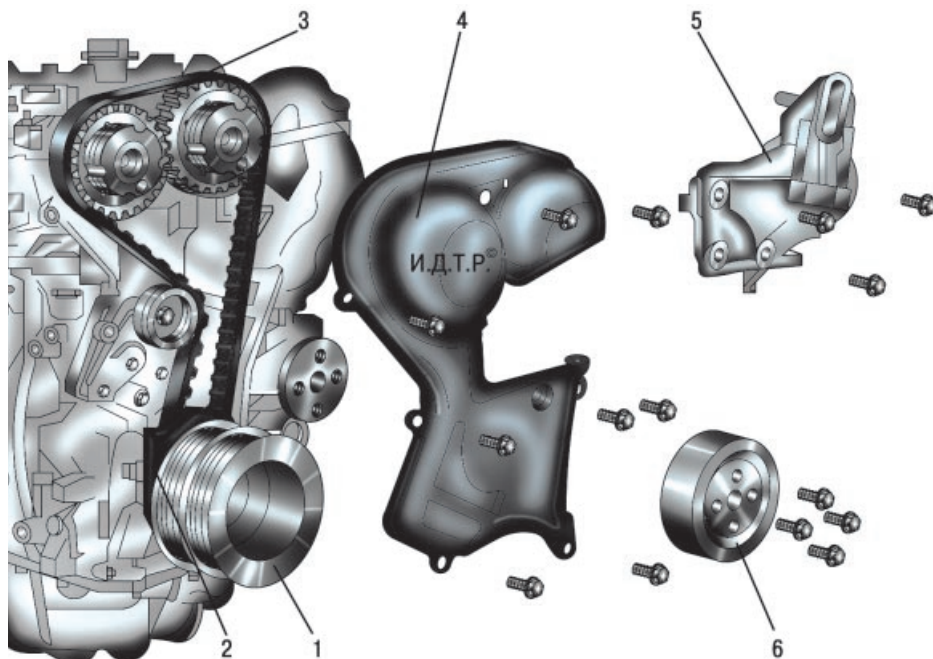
Узлы двигателя, снимаемые при замене ремня привода газораспределительного механизма: 1 – шкив коленчатого вала; 2 – нижняя крышка привода газораспределительного механизма; 3 – ремень привода газораспределительного механизма; 4 – передняя крышка привода газораспределительного механизма; 5 – кронштейн правой опоры подвески силового агрегата; 6 – шкив водяного насоса
